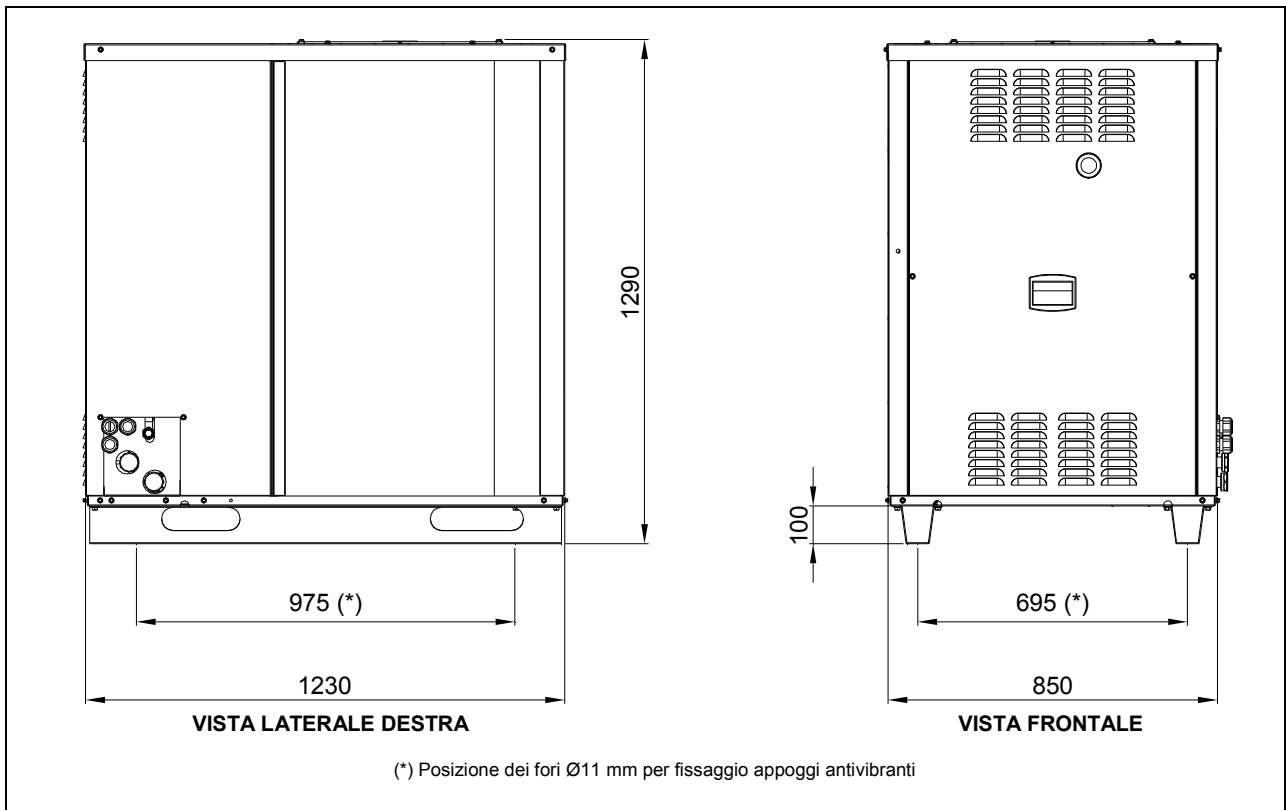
Dimensioni GA ACF - vista frontale e laterale (quote espresse in mm)
